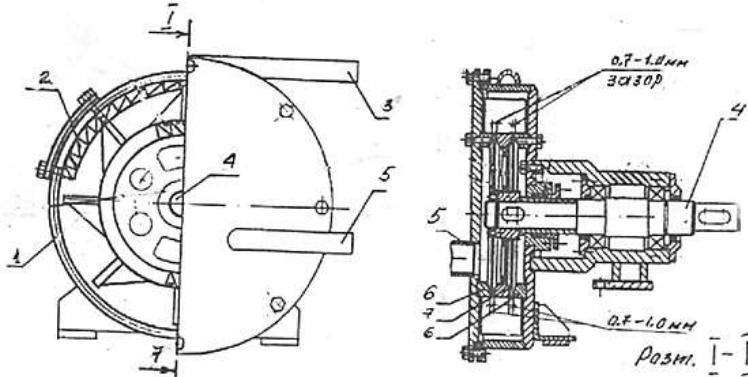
Гідромлин-змішувач: 1. корпус; 2. жорна; 3. вихідний патрубок; 4. вал; 5. вхідний патрубок; 6. бокові жорна; 7. центральний жорнов (ротор)
